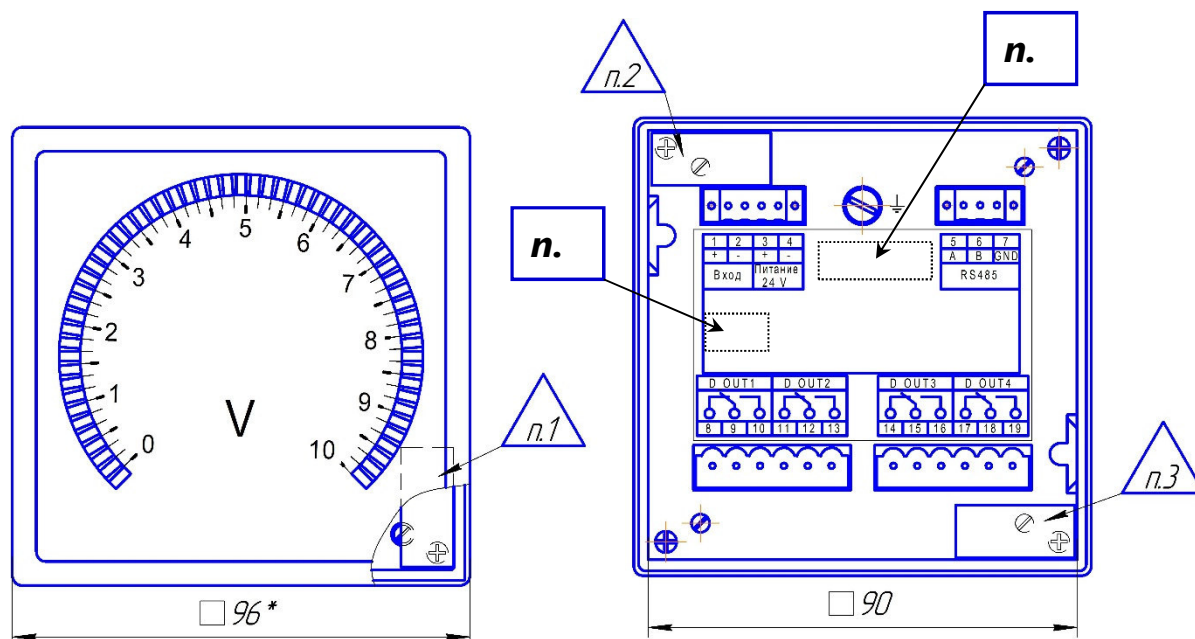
Общий вид приборов Щ23.7, Щ23.8
